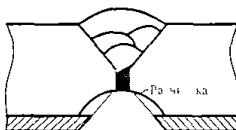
Порядок выполнения ручной дуговой сварки (по I варианту)
